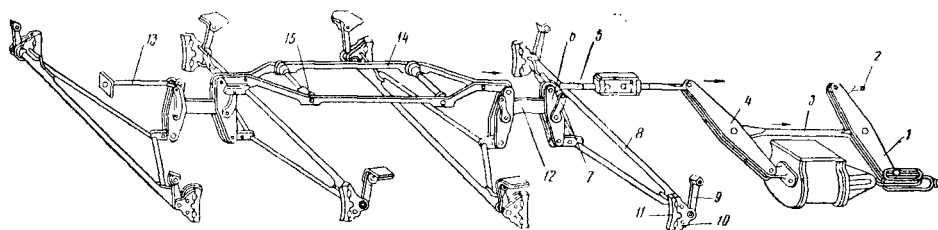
Схема рычажной передачи тележки моторного вагона;
